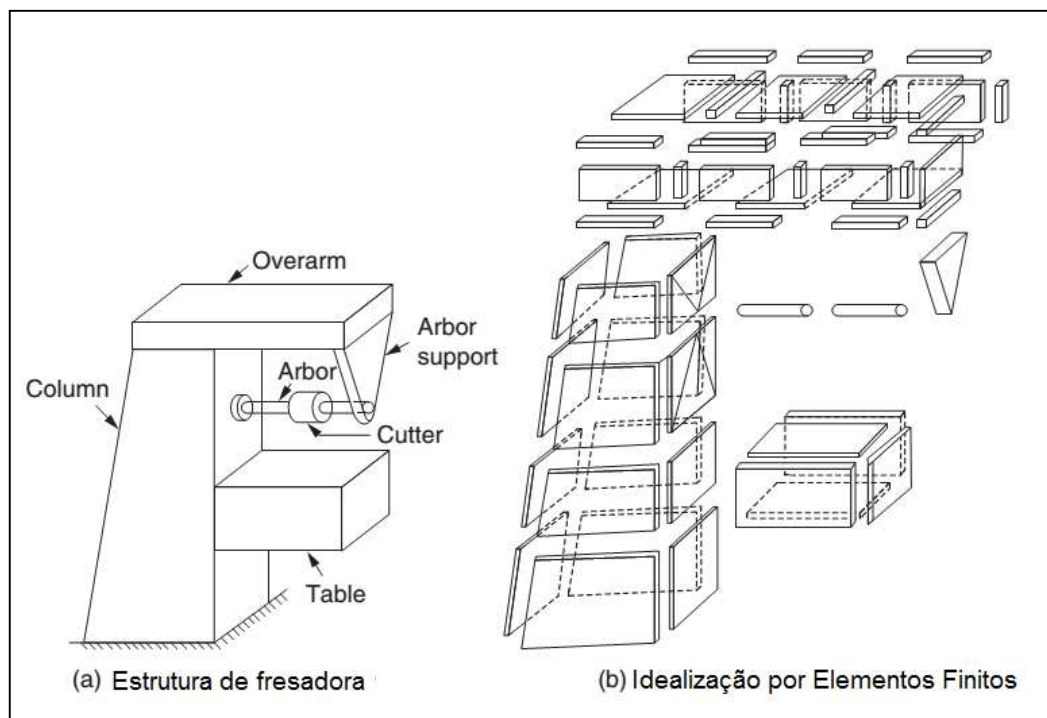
Exemplo da aplicação de Elementos finitos [7]
